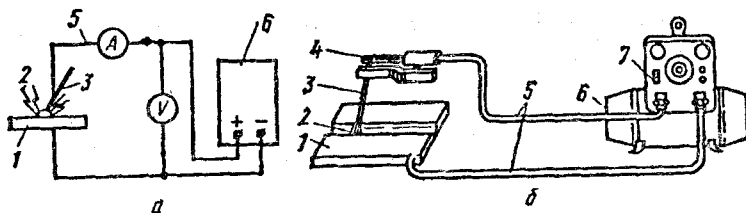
Компоновка сварочного поста и схема питания дуги (на постоянном токе): *a* — электрическая схема; *б* — общая компоновка поста для сварки; 1 — изделие; 2 — сварочная дуга; 3 — электрод; 4 — электрододержатель; 5 — сварочные провода; 6 — источник питания; 7 — щит с приборами контроля и регулирования параметров режима сварки
